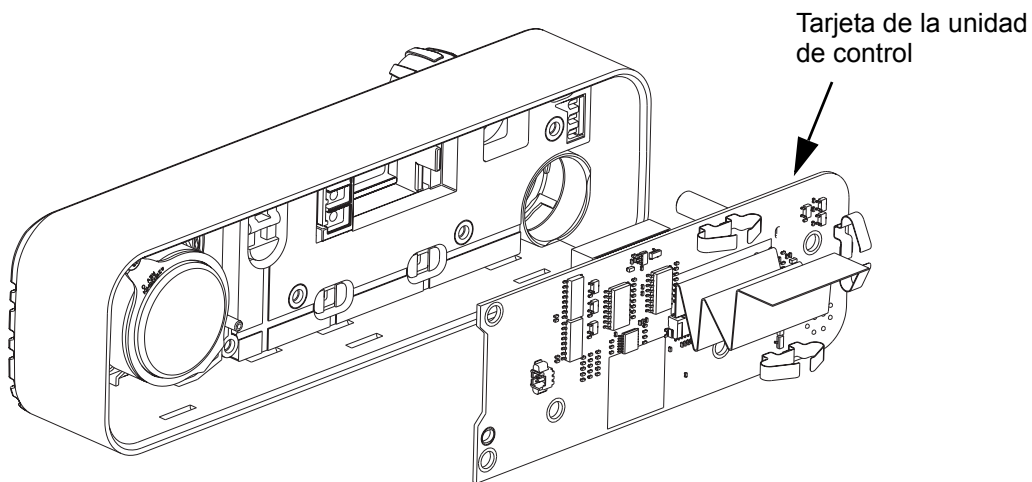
Desmontaje de la tarjeta de la unidad de control
